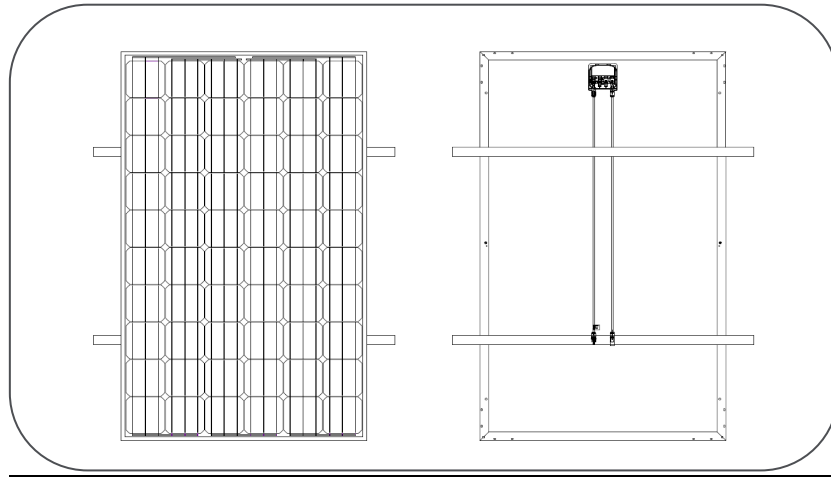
Vue de dessus et vue arrière du module installé sur une structure de montage parallèle
